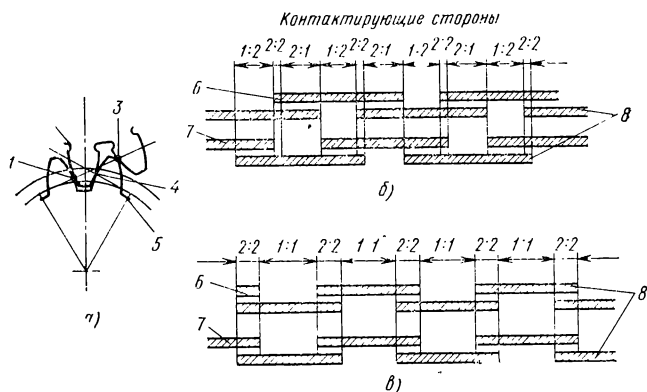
Схема одновременного зацепления зубьев шевера и колеса:
